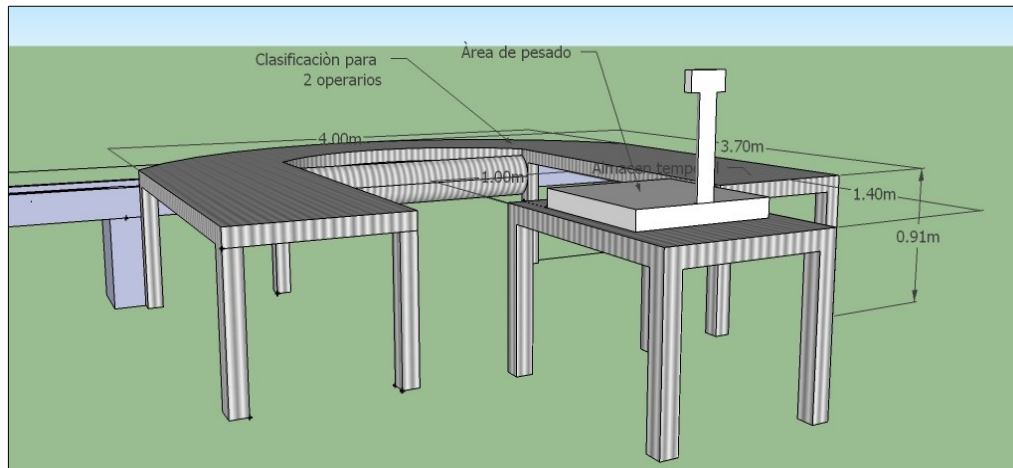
Vista de planta, para estación de trabajo remodelada
